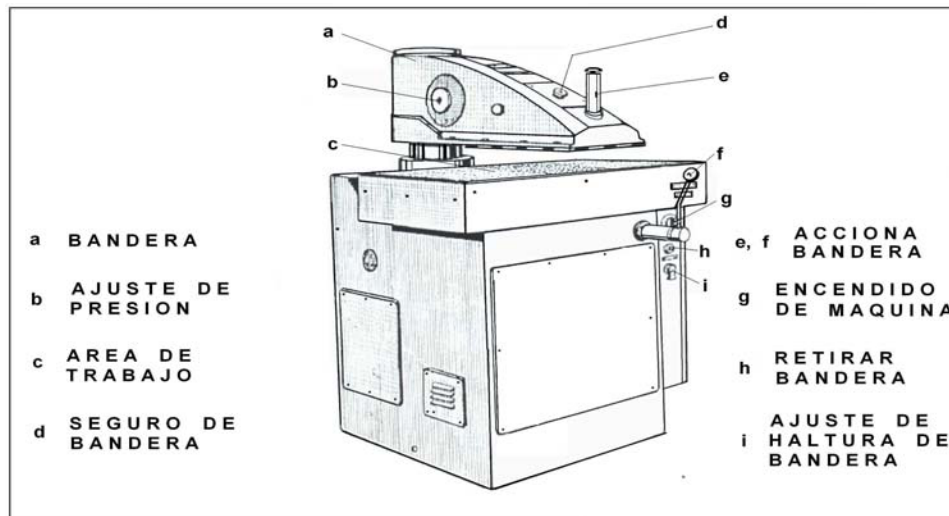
Dibujo esquemático de una máquina hidráulica.
